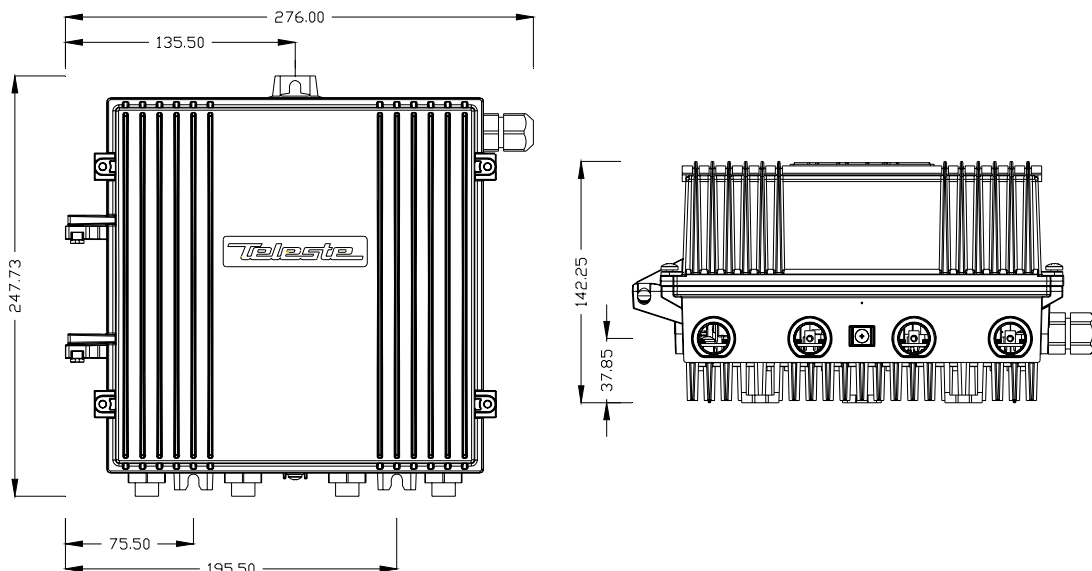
Размеры корпуса AC8000 – виды сверху и сбоку
